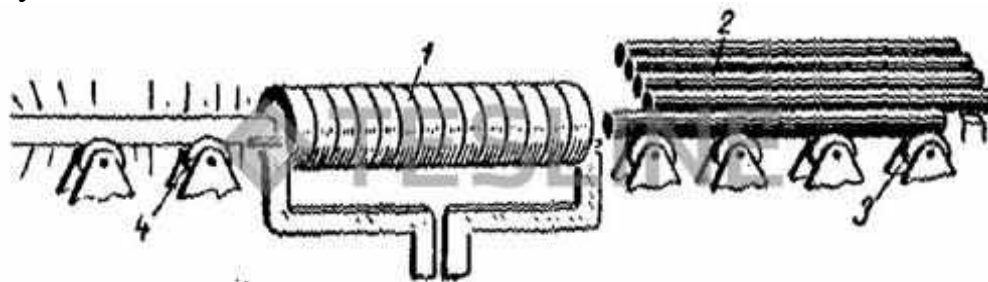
Схема методического нагревателя с непрерывным движением заготовок:
